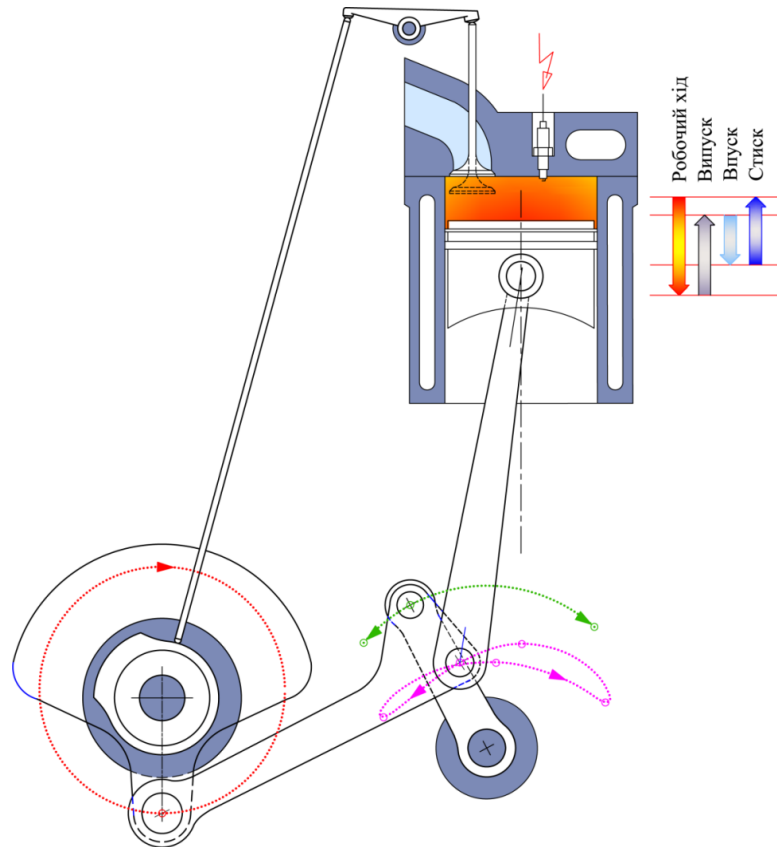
Схема хитневого механізму з двома верхніми та двома нижніми мертвими положеннями
